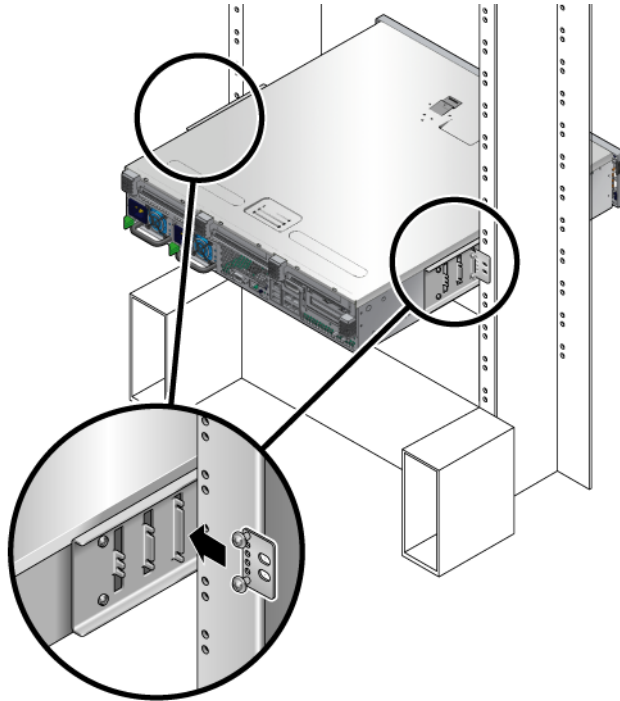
Installation de la plaque arrière sur le support latéral
